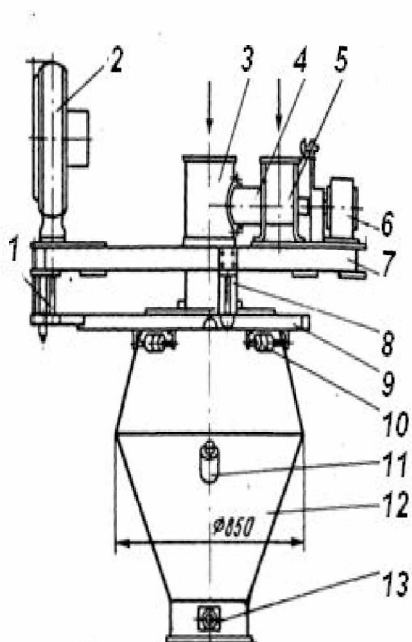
Напівавтоматичний дозатор борошна Ш2-ХДА: 1 – тяга; 2 – циферблатний показчик; 3 – патрубок подавання борошна в бункер; 4 – шнековий досипний пристрій; 5 – патрубок досипаного пристрою; 6 – привід досипаного пристрою; 7 – рама; 8 – підвіски; 9 – ваговий ричаг; 10 – тарні вантажі; 11 – вібратор; 12 – бункер; 13 – заслінка
